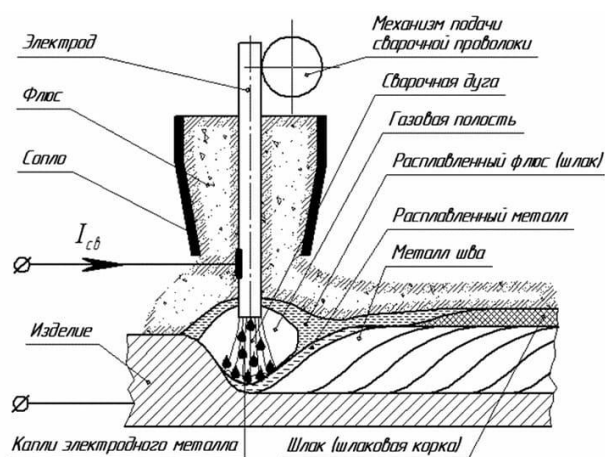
Схема дуговой сварки под флюсом
